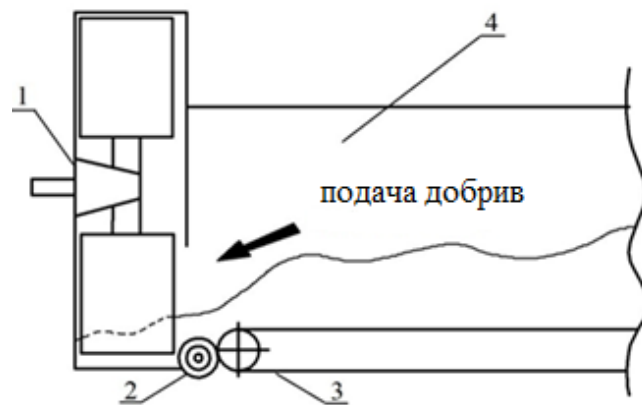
Схема подання добрив до робочого органу де 1 - пневмомеханічний робочий орган роторного типу; 2 - шнек-живильник; 3 - стрічковий транспортер; 4 - кузов розкидання з добривами
